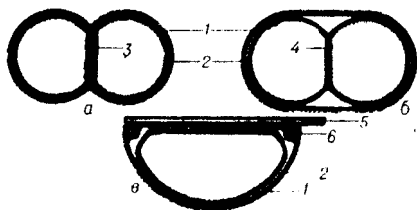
Поперечное сечение надувных гондол: а – двухбаллонной с перегородкой в чехле; б – двухбаллонной с перегородкой в баллоне; в – однобаллонной; 1 – чехол; 2 – надувной баллон; 3 – перегородка в чехле; 4 – перегородка в баллоне; 5 – балка; 6 – стрингер
